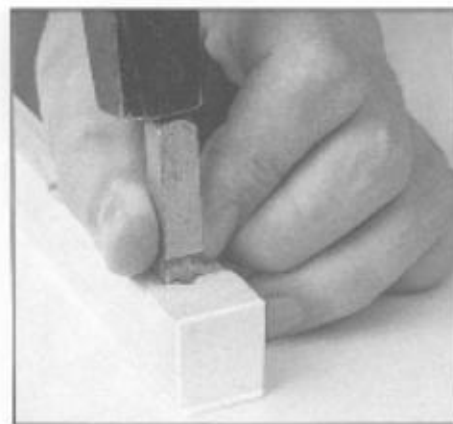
durch Klopfen mit einem Spezialwerkzeug oder ...
